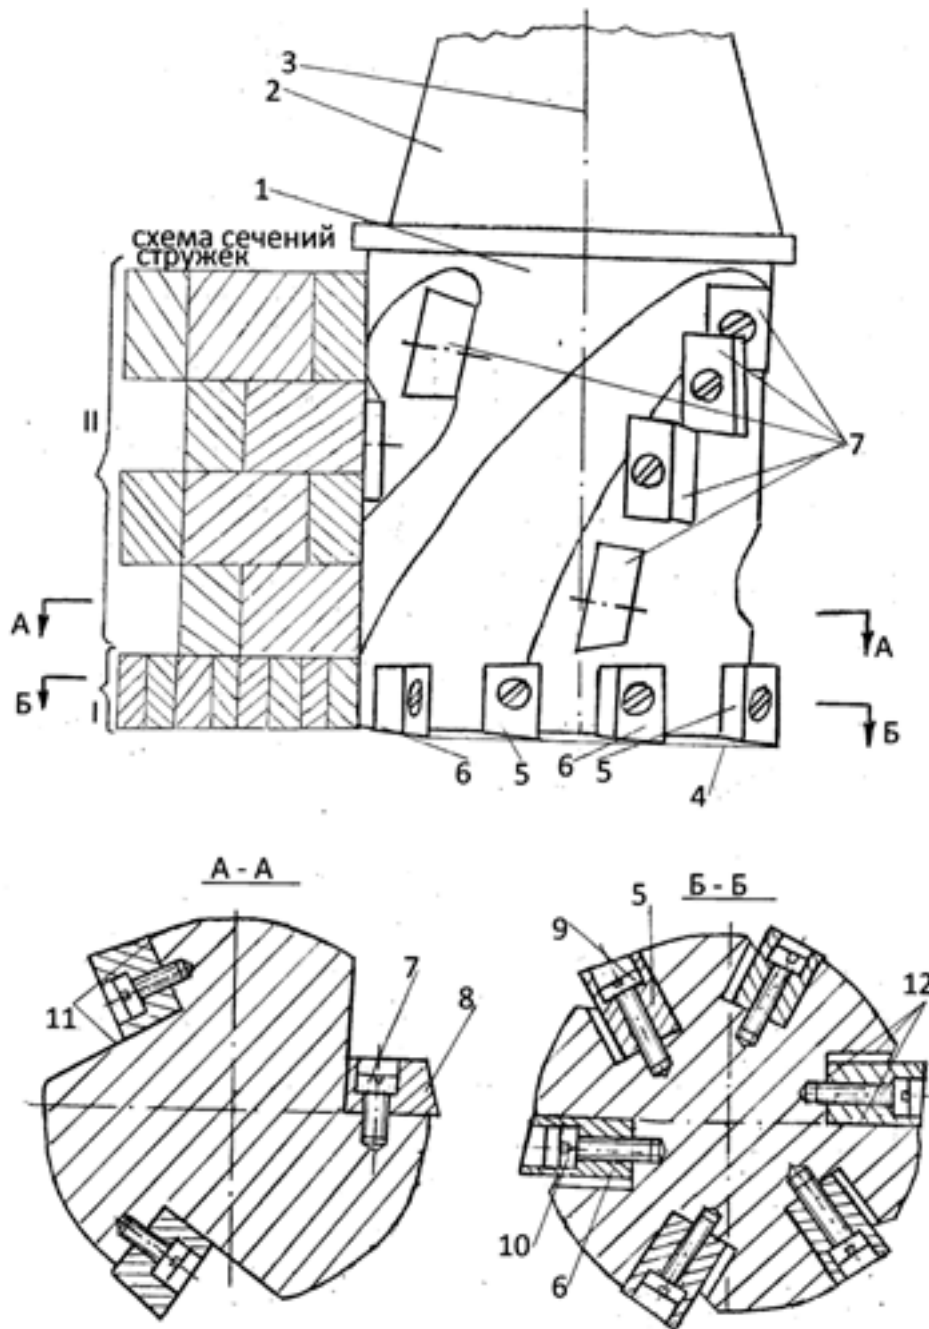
Торцово-цилиндрическая фреза с дополнительными торцовыми пластинами в торцовой части
